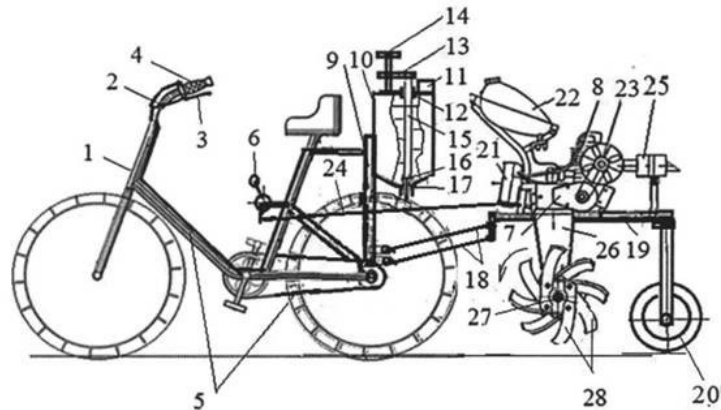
Схема агрегата для подготовки почвы под посадку риса в Бурунди — общий вид сбоку агрегата в транспортном положении
